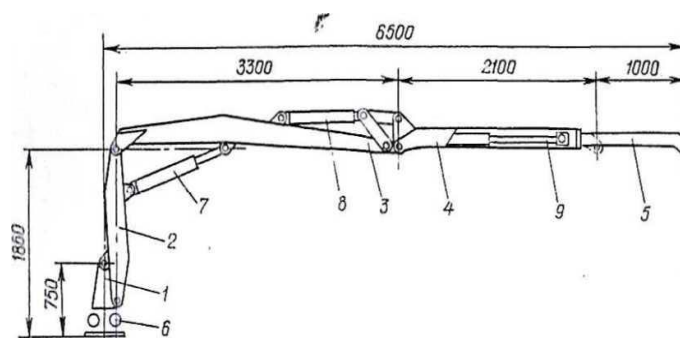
Манипулятор модульный лесохозяйственный ММЛ-6,5 (базовая модель): 1– опорно-поворотное устройство; 2 – колонна; 3– стрела; 4– рукоять; 5 – удлинитель; 6, 7, 8, 9— гидроцилиндры
